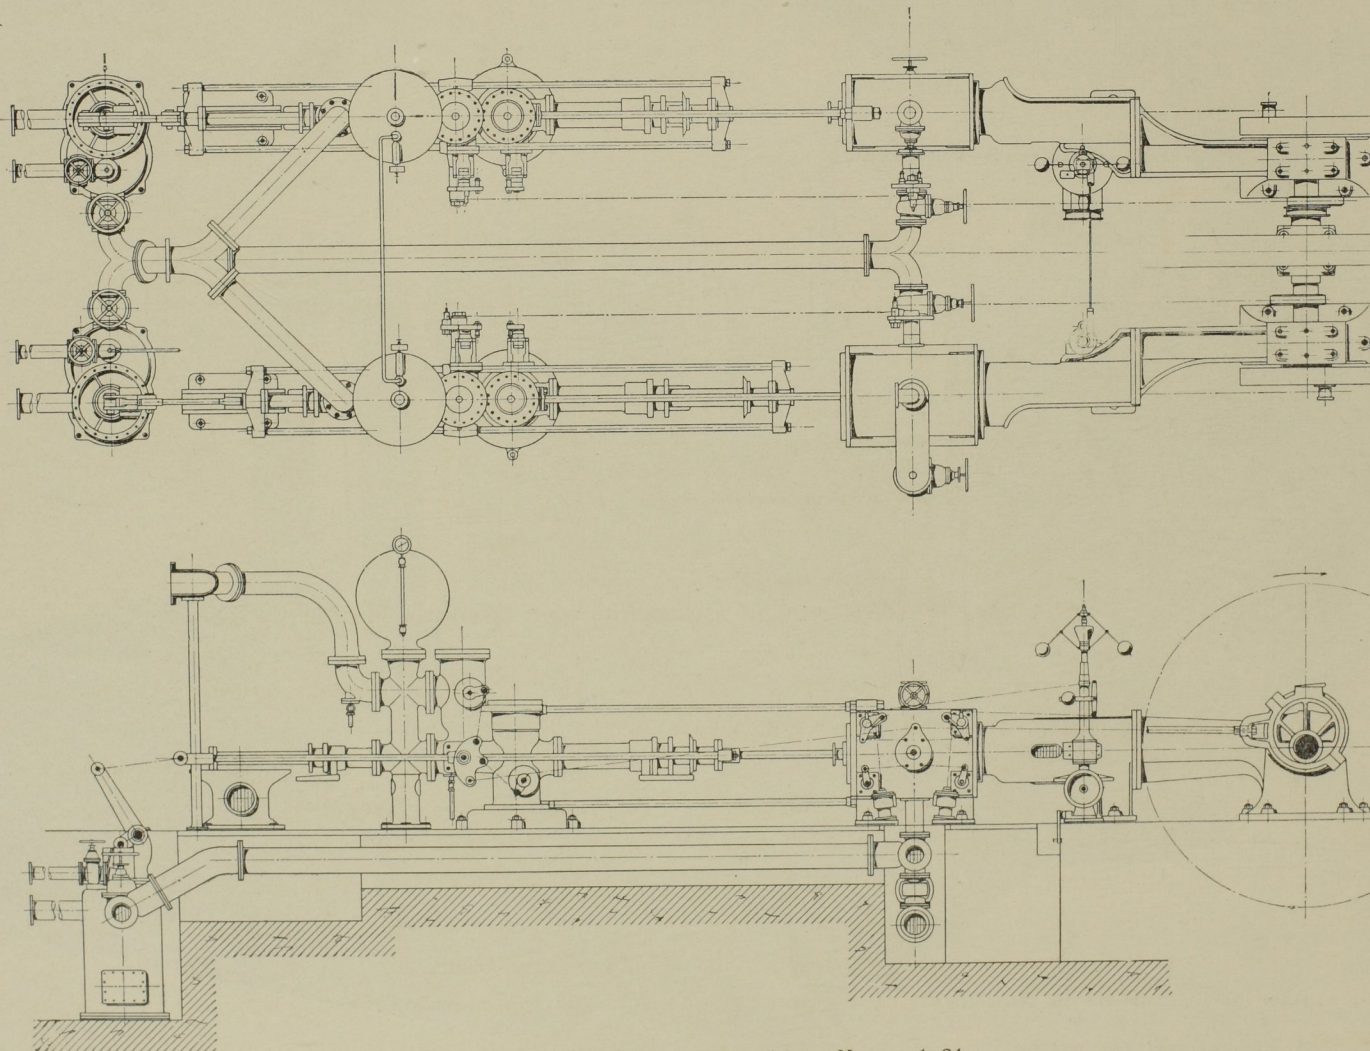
Seitenansicht und Grundriss. Masst. 1:64.
